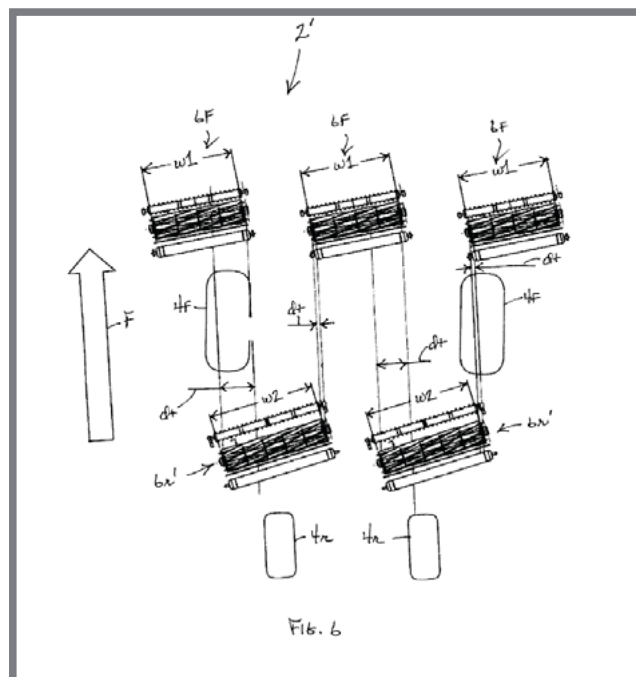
Geometrie přesahů vřeten 3 + 2 [26]
